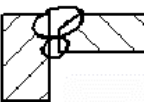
Изображение точечных сварных швов, размеры сварной точки
